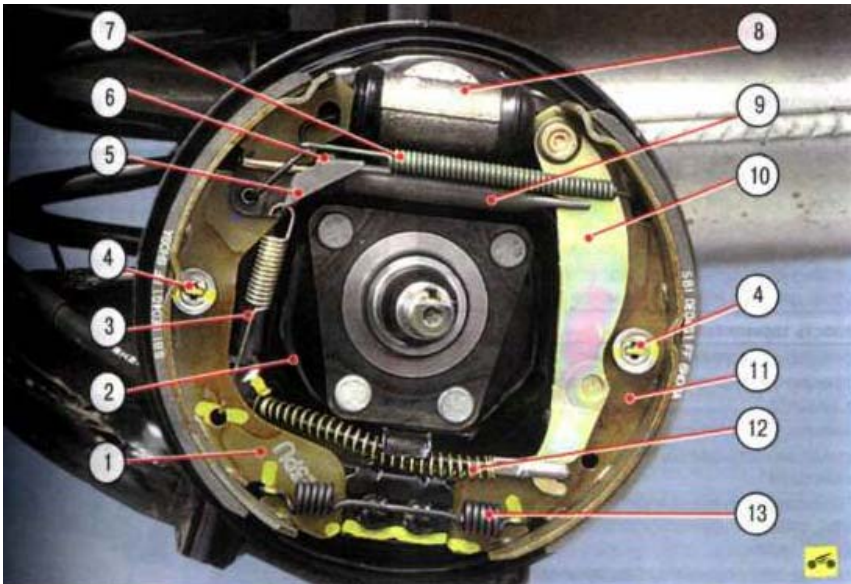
Тормозный механизм заднего колеса: 1 - передняя тормозная колодка. 2 - щит тормозного механизма; 3 - пружина рычага регулятора зазоров; 4 - опорные стойки; 5 - рычаг регулятора зазоров; 6 - регулятор зазоров; 7 - верхняя стяжная пружина; 8 - рабочий цилиндр; 9 - распорная планка; 10 - разжимной рычаг привода стояночного тормоза; 11 - задняя тормозная колодка; 12 - трос привода стояночного тормоза; 13 - нижняя стяжная пружина.
